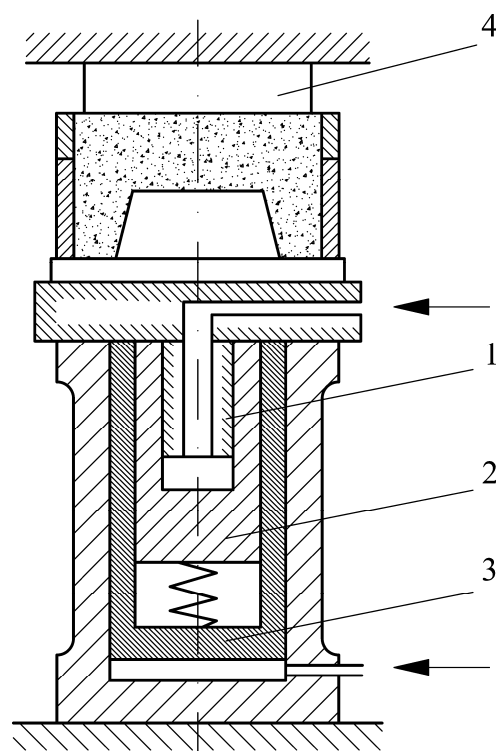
Схема механизма для уплотнения литейных форм встряхиванием с одновременным прессованием: 1 – встряхивающий поршень; 2 – амортизатор; 3 – прессовый поршень; 4 – прессовая колодка
